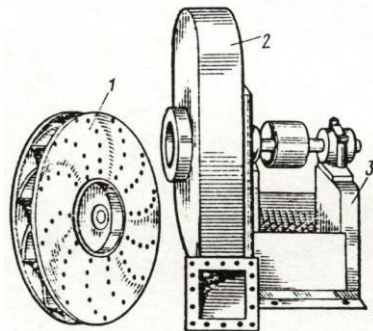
Вид радіального вентилятора (варіант): 1-лопаткове колесо; 2-спіральний корпус; 3-станина
